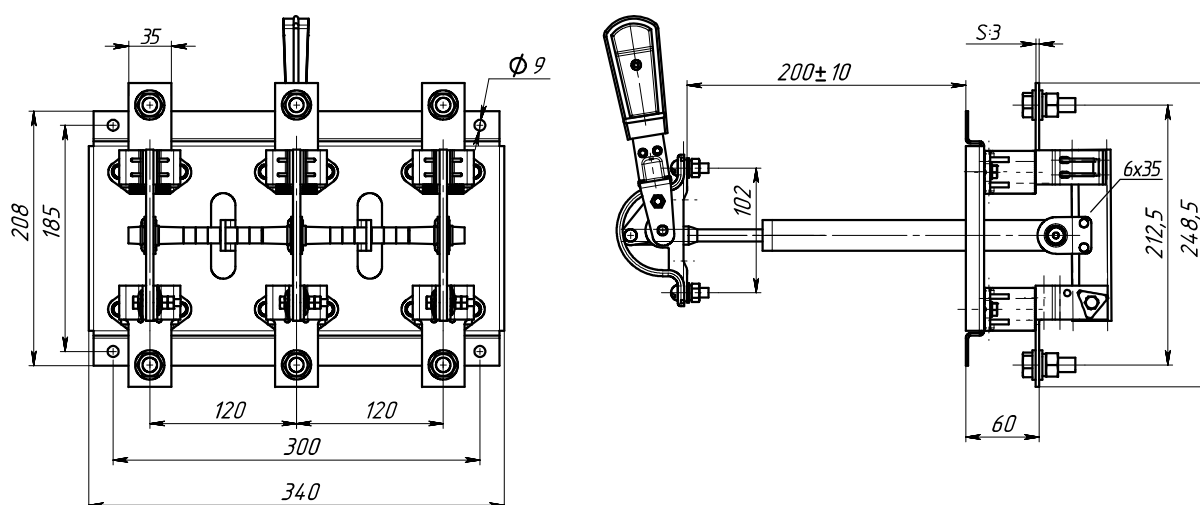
Разъединитель серии P с центральным приводом РЦ-6, на номинальный ток 630 А
